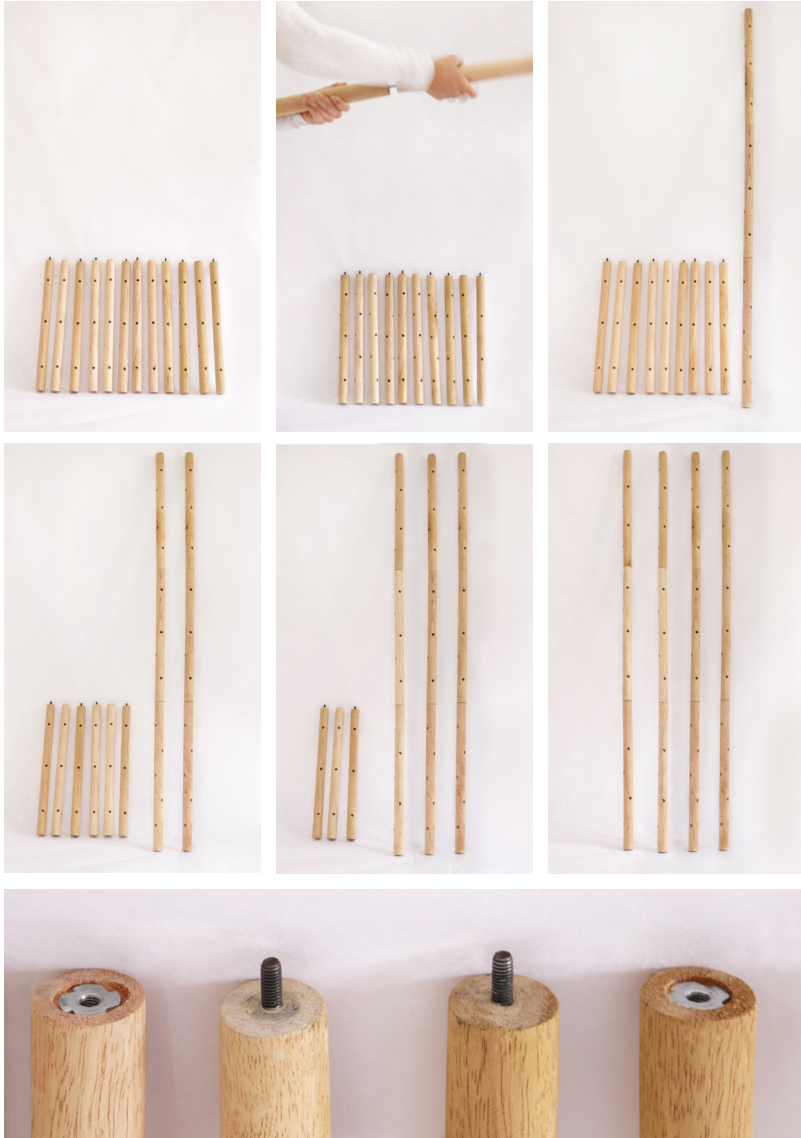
Prototipo 2, alternativa de solución técnica de armado.
